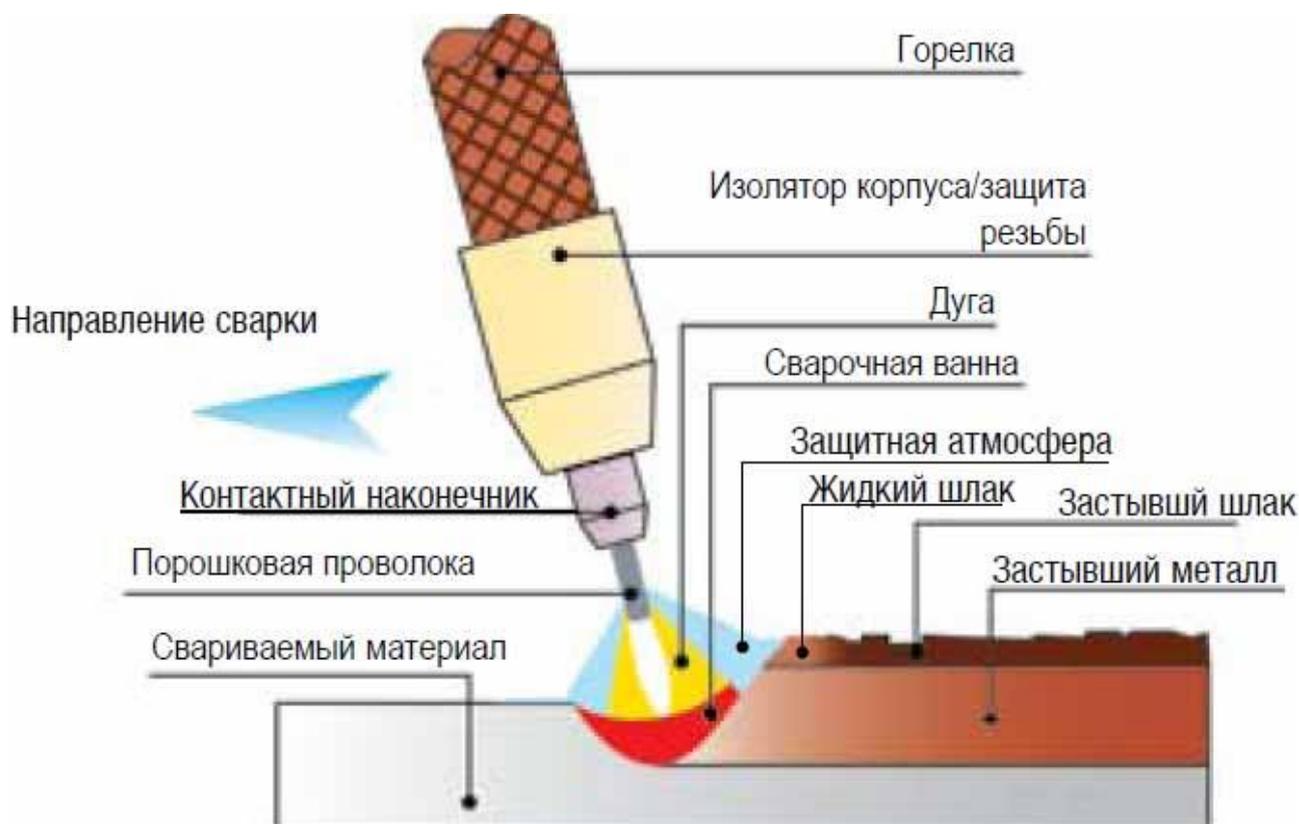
Способ сварки порошковой проволокой
